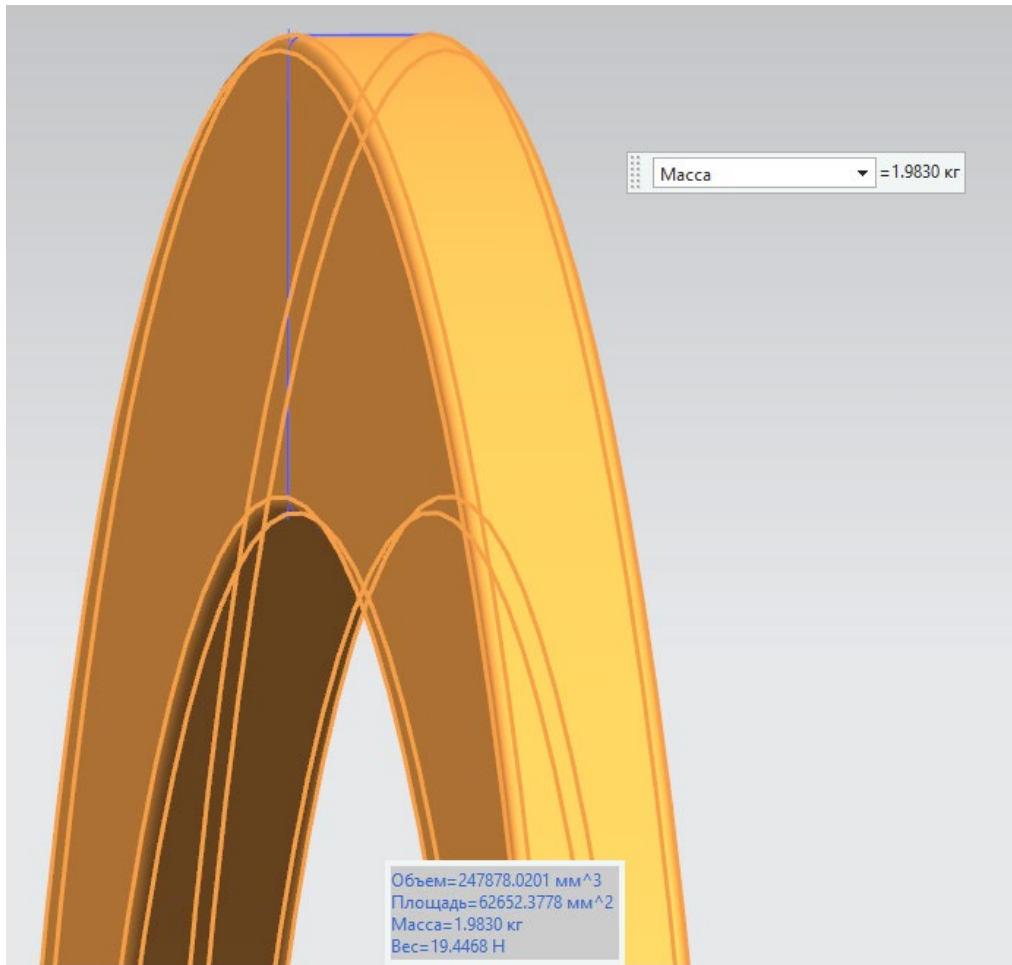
3D модель заготовки штамповки КГШП
